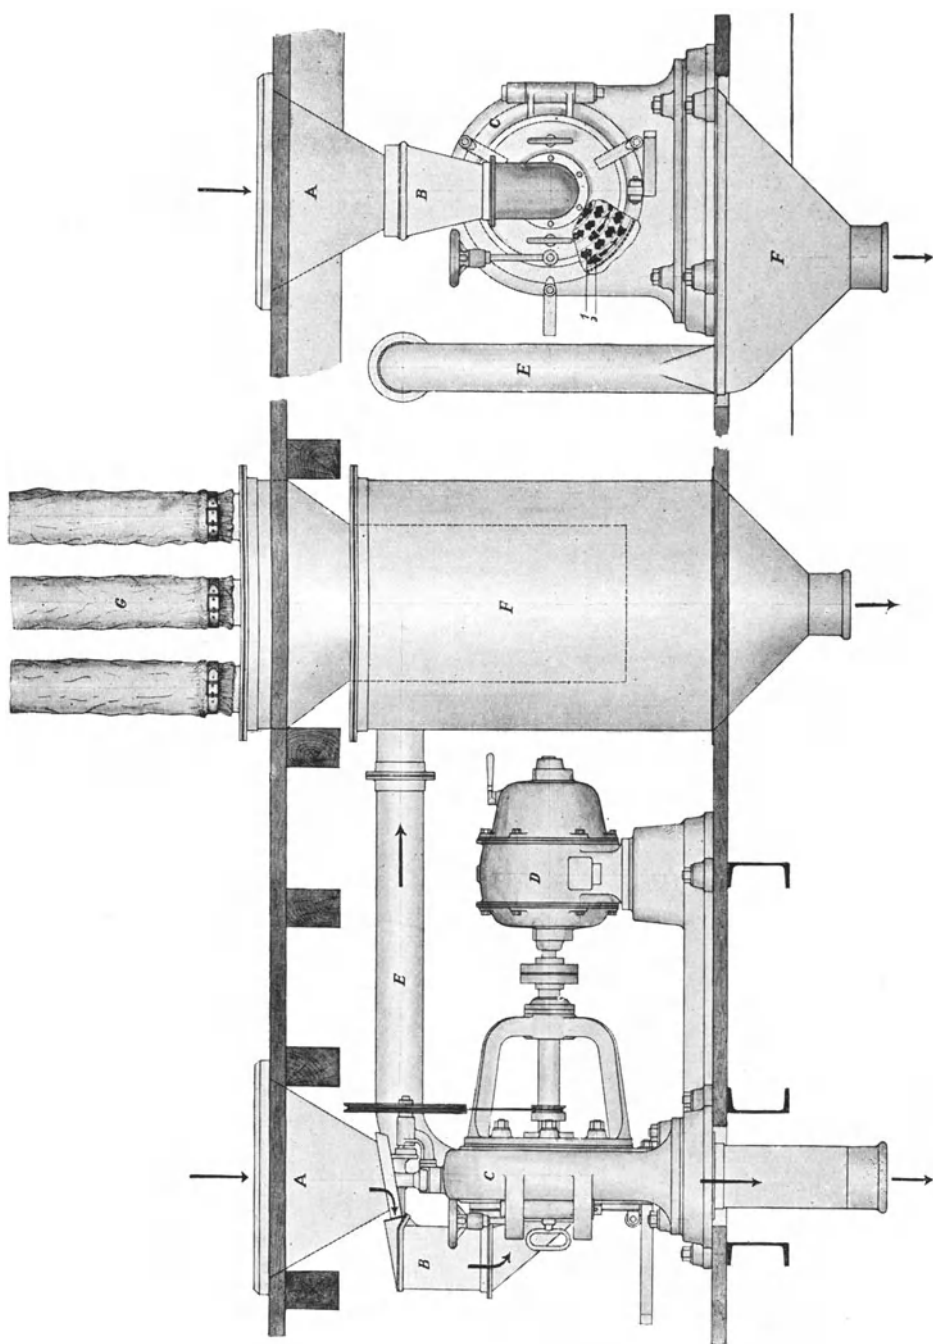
Desintegrator für Farbstoffe (Maßstab 1:20).
